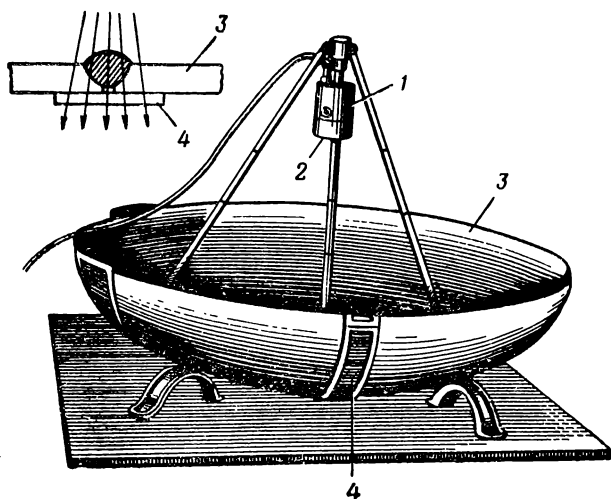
Просвечивание сварного шва сферической сварной детали (вверху слева показана схема просвечивания):
